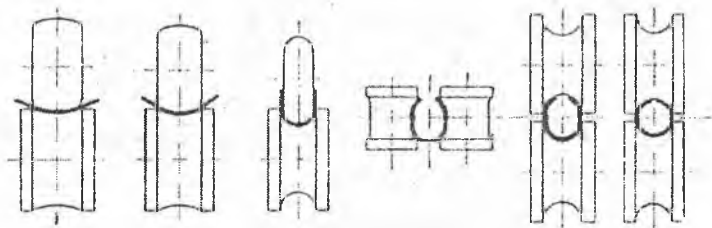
Схема формовки полосы в трубную заготовку на многоклетьевом формовочном стане
